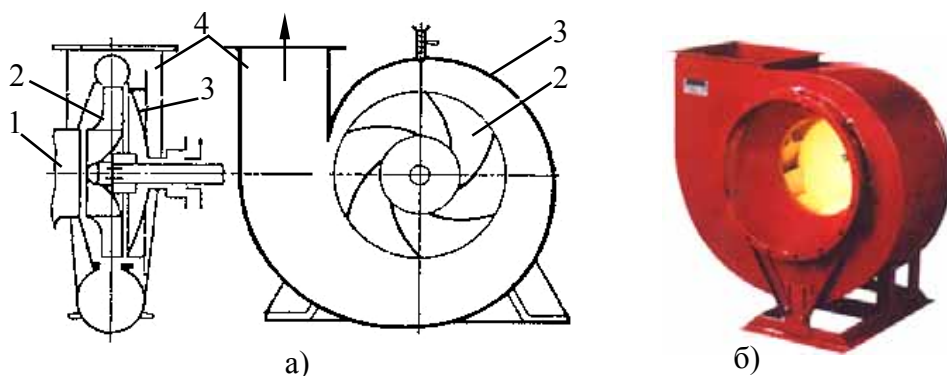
Конструкція (а) та зовнішній вигляд (б) відцентрового нагнітальника: 1 – всмоктувальний патрубок; 2 – робоче колесо; 3 – камера; 4 – нагнітальний патрубок
